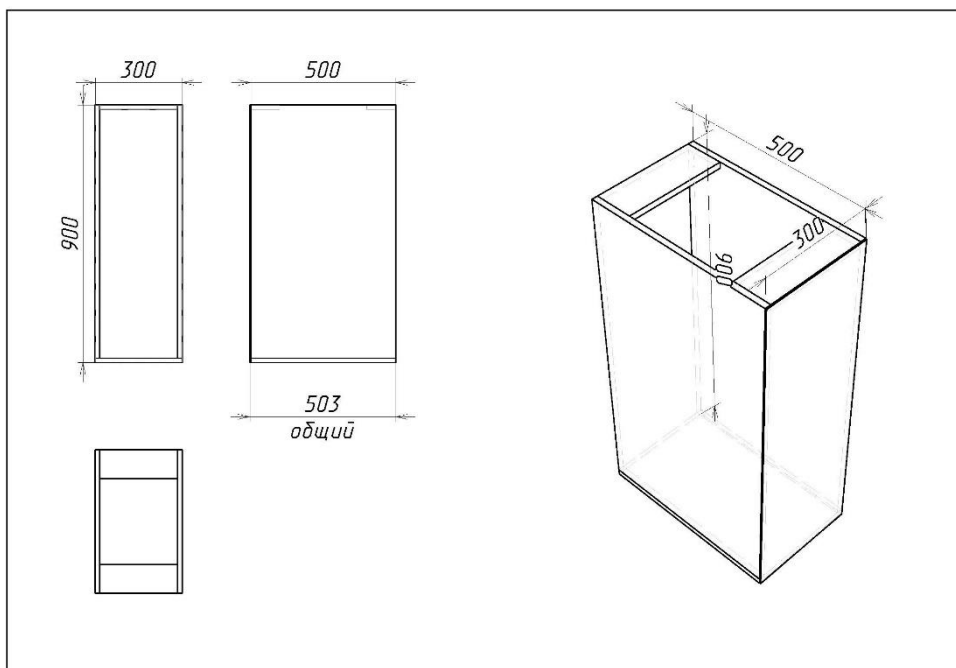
Установка задней стенки в накладку в корпус с вкладными крышкой и дном (БМ)
